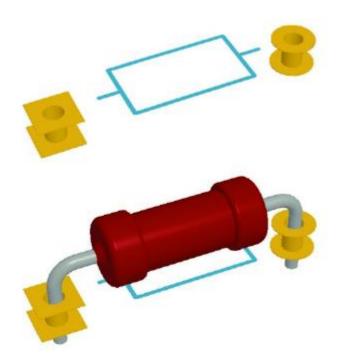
трехмерный вид посадочного места и твердотельная модель резистора
